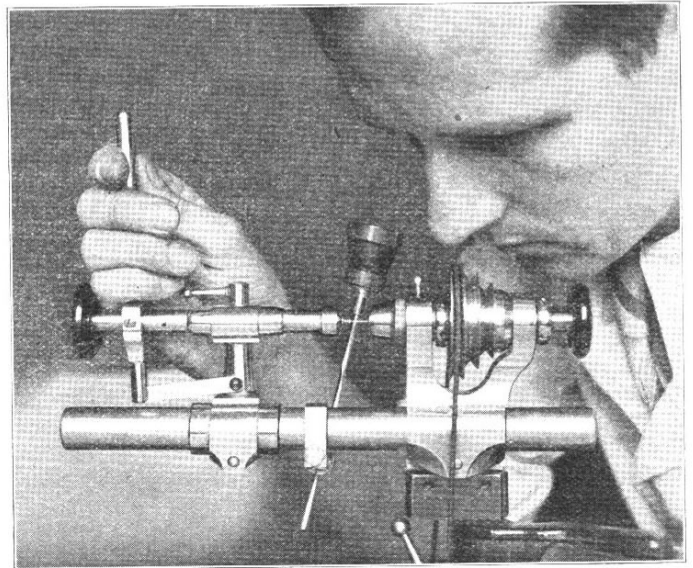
So sieht die Bohreinrichtung aus. Links der Reitstock mit Amerikaner Zange mit eingespanntem Federkern. Rechts der Spindelstock mit dem Bohrer. In der Mitte eine Lupe mit Halter (1 Zeichn., 1 Aufn. privat)
